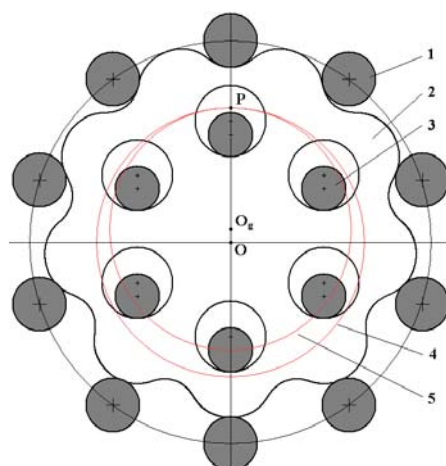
Планетарный редуктор с цевочным зацеплением:
